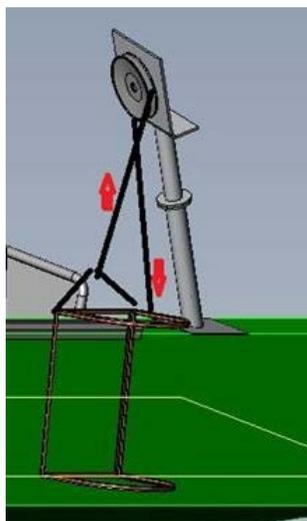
Haleur incliné pivotant en hauteur-travail optimal
